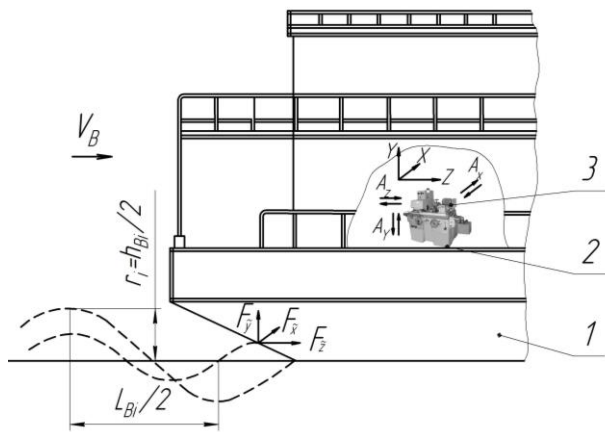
Схема расположения круглошлифовального станка на участке ПМ:
